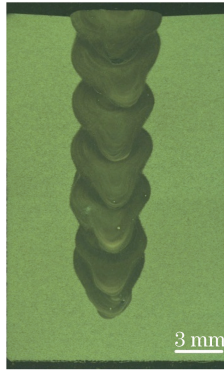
深度为 17 mm 的超窄间隙坡口激光填丝多层焊焊缝截面形貌
